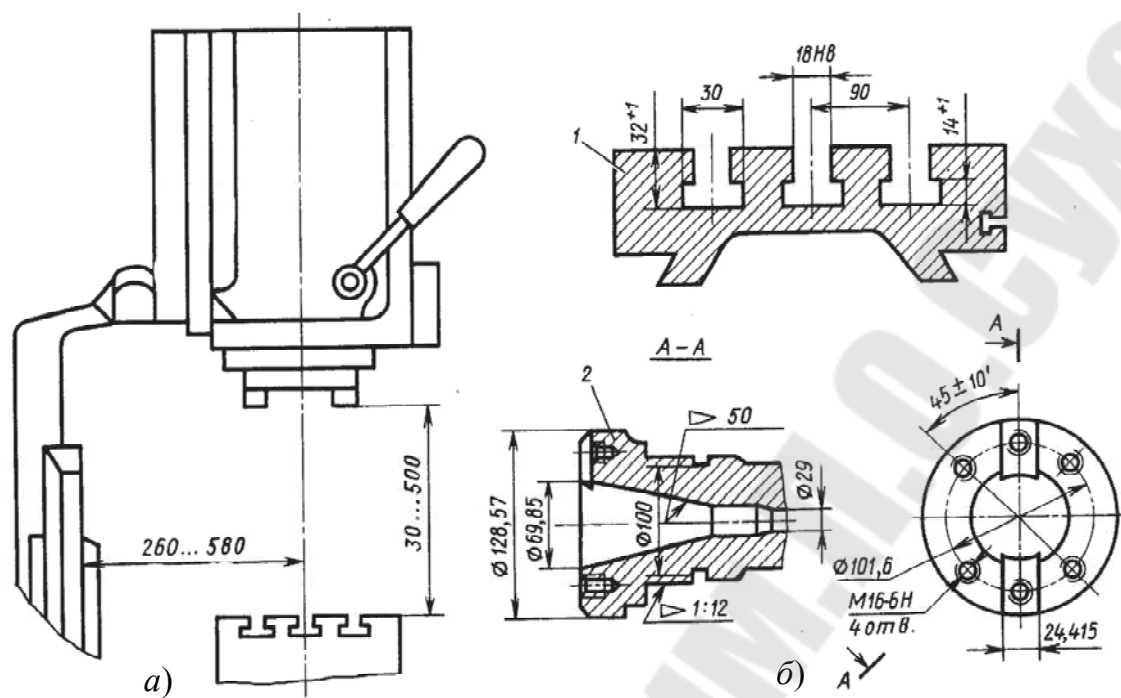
Эскиз рабочего пространства станка модели 6P13Б:
